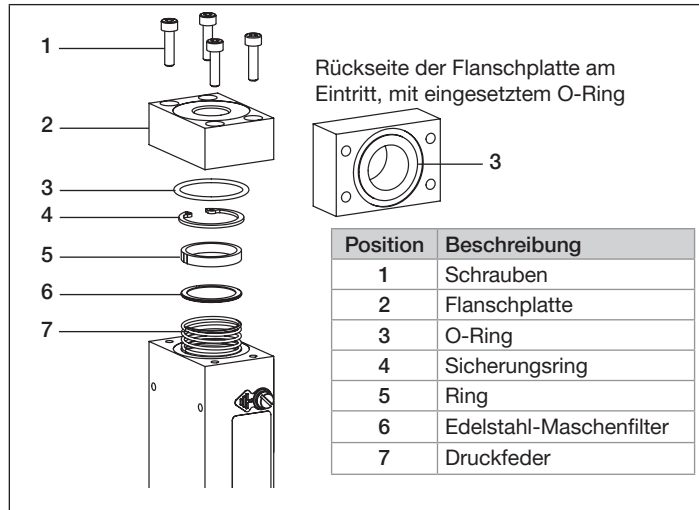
Explosionsansicht – Teile im Kontakt mit dem Betriebsmedium
